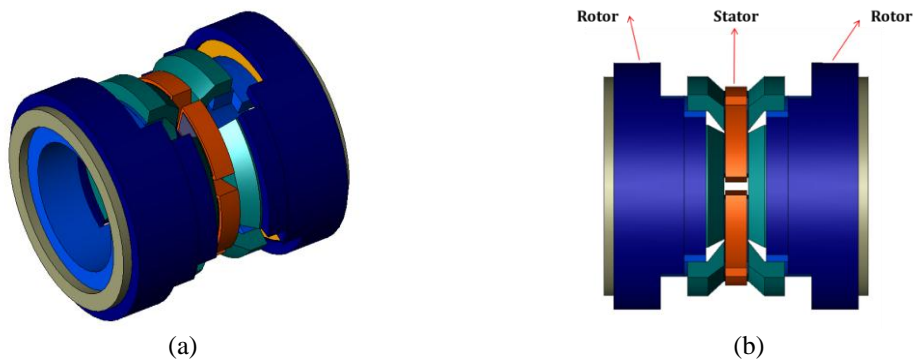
Vue en perspective (a) et vue latérale (b) de l'alternateur à griffes axiales (AGA)
